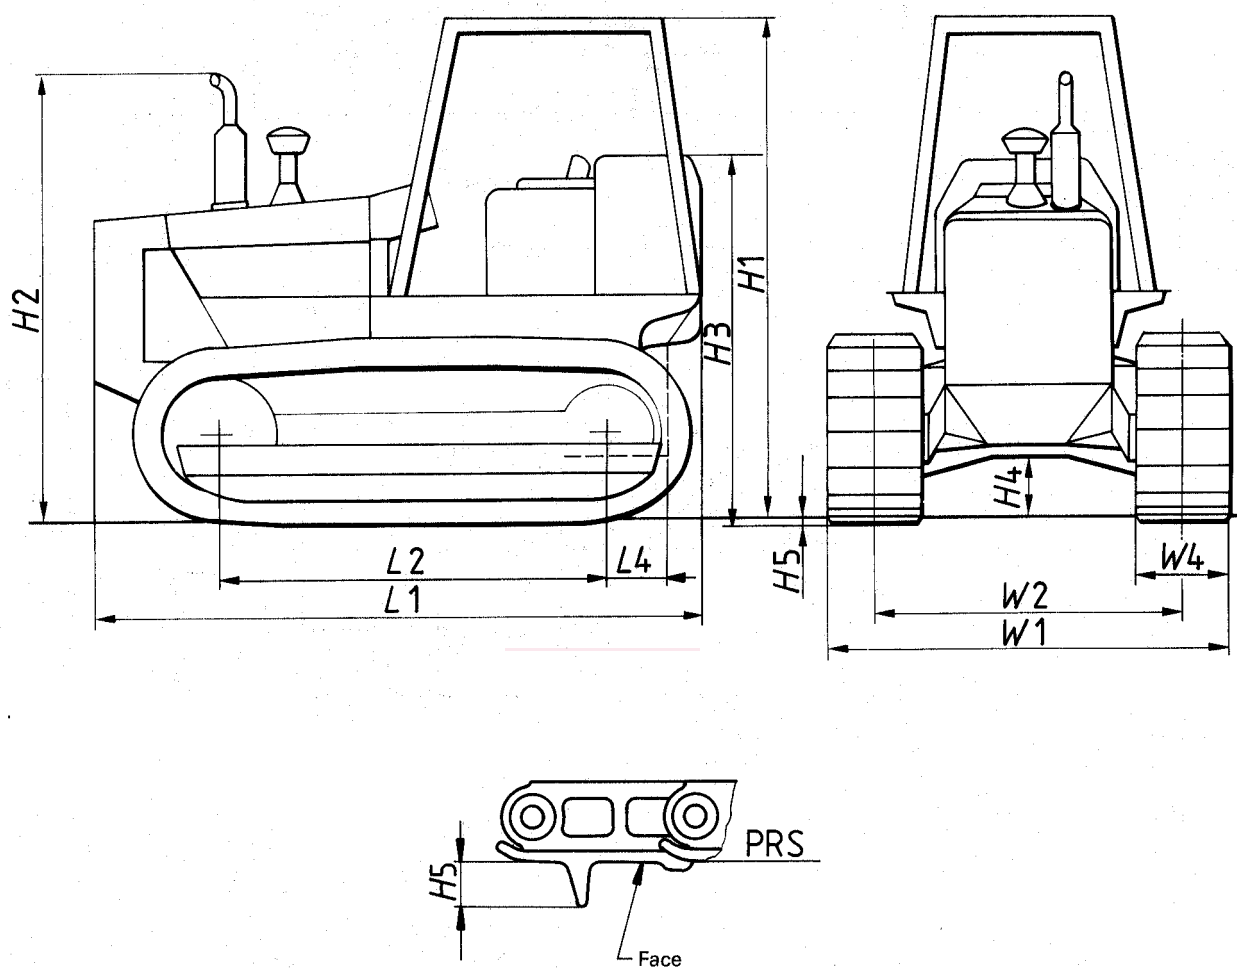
Dimensions de l'engin de base (tracteur à chenilles)
